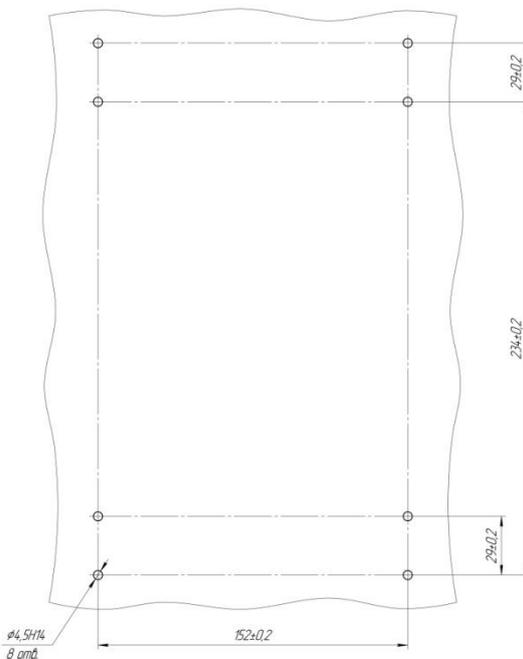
Габаритные и присоединительные размеры устройства РС830-ФКС-ЖД при внешнем монтаже, обеспечивающем его поворот влево/вправо
